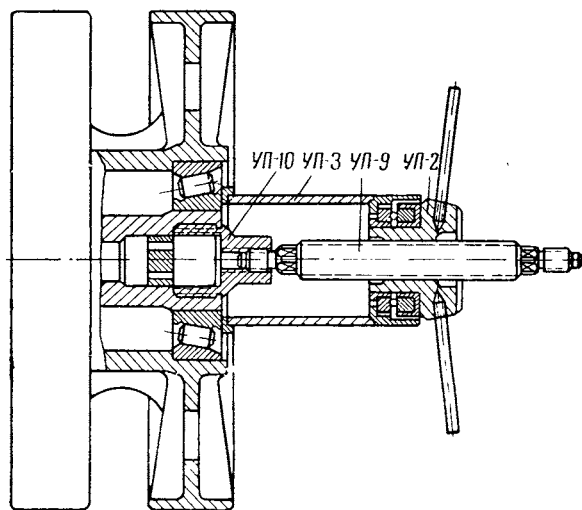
Универсальное приспособление 48001-1-074 УП, напрессовка направляющего колеса и опорного катка
